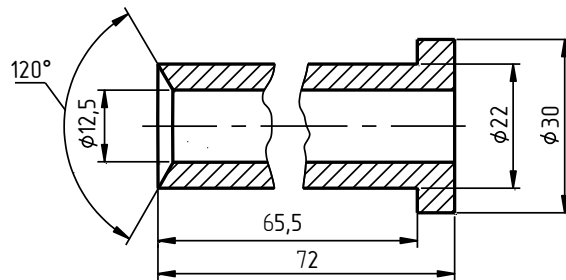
Размерную линию не прерывают при изображении детали *разрывом
